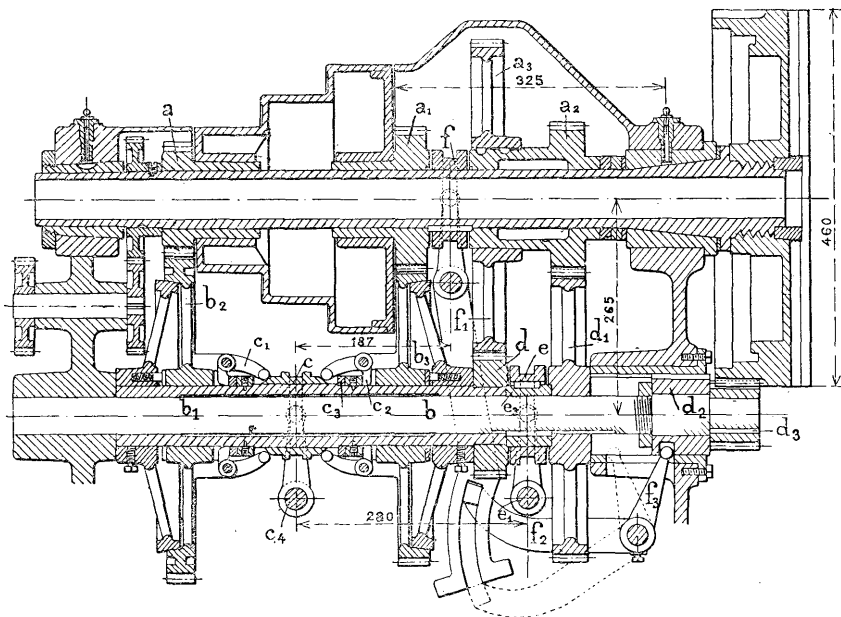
Coupe de la poupée fixe du tour Conradson.
